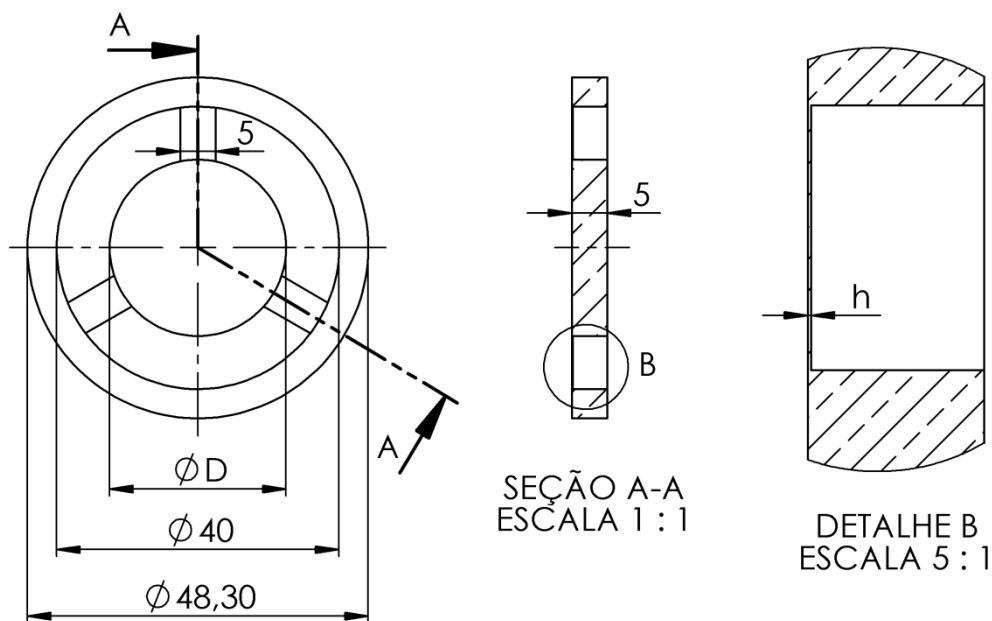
Desenho técnico do ressonador (dimensões em mm)
